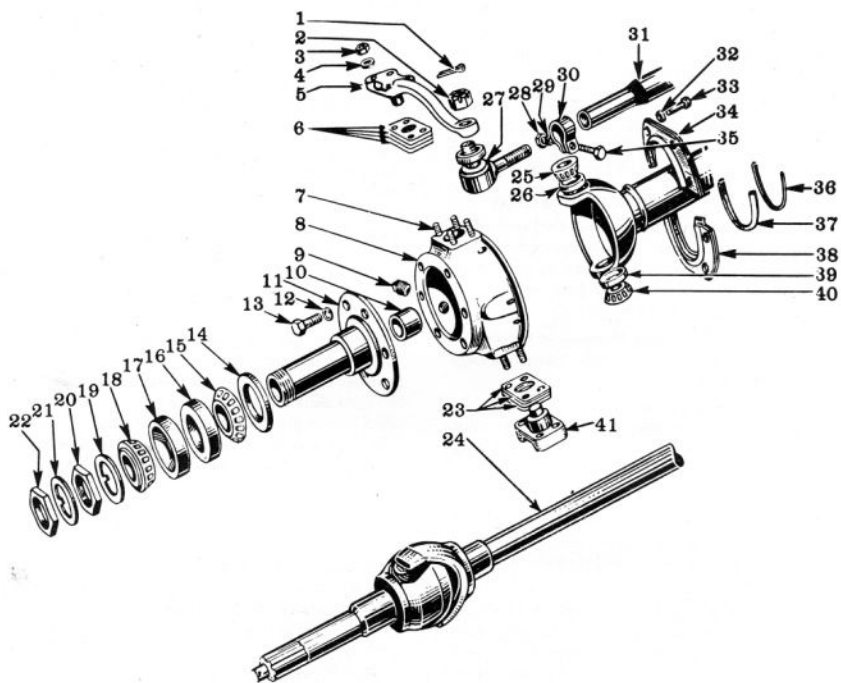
Pont avant, pivot de fusée et roulements de roue (joints de cardan Bendix).
